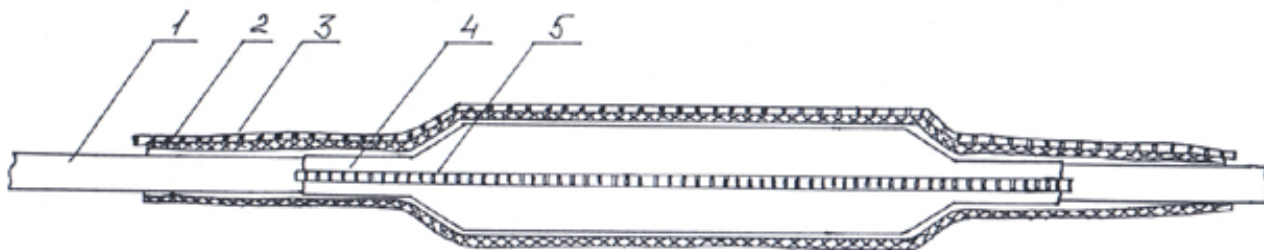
Усадка наружной манжеты на муфту, смонтированную на кабеле с защитным шлангом типа «Шп». После усадки наружная манжета должна перекрывать внутреннюю с каждой стороны не менее чем на 70 мм. На муфтах МПВ металлические застёжки манжет могут находиться одна над другой или так, как показано на данном рисунке:
